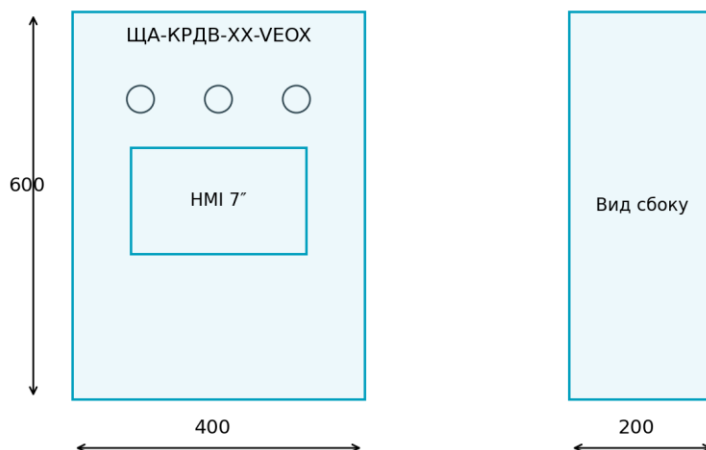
Габариты корпуса. Крепёжные размеры и кабельные вводы — по чертежу поставляемого щита.
